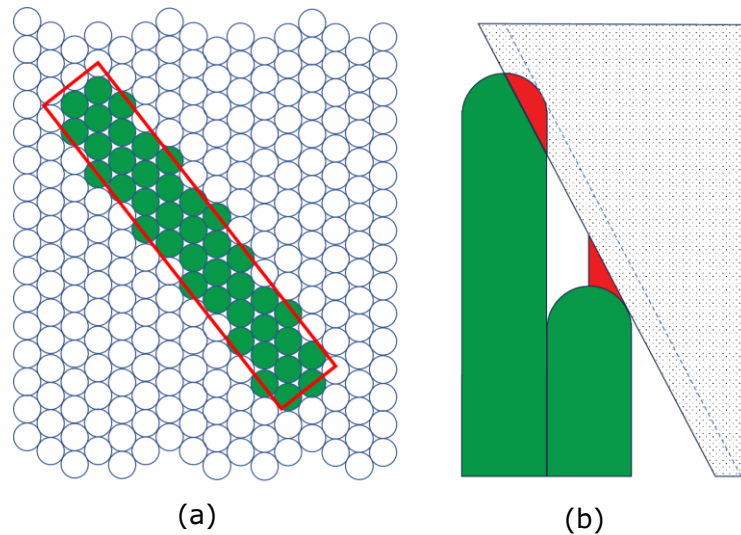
a) Draufsicht einer Bauteilgeometrie (rot) und der verwendeten Formstifte (grün)
